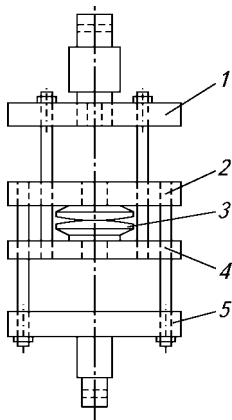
Схема приставки (реверсора) для испытания пластмасс на сжатие:
